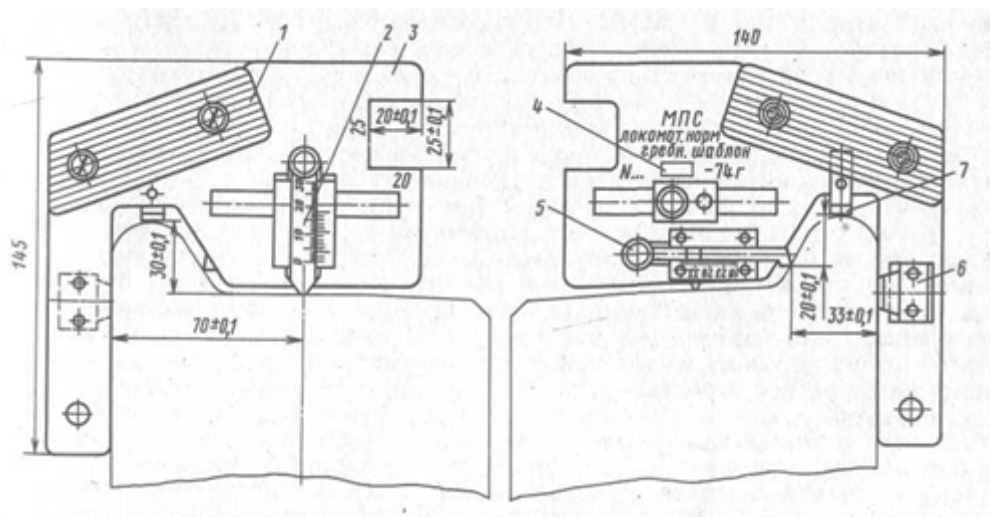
Абсолютний шаблон для вимірювання прокату та товщини гребня коліс: 1 — планка ручки; 2—вертикальний движок; 3—основа; 4—клейма заводу-виготовлювача; 5—горизонтальний движок; 6—упорний кутник; 7—упорна ніжка
